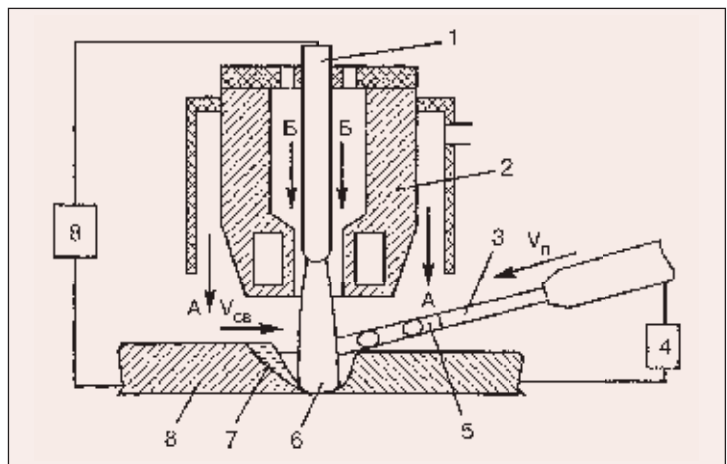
Схема плазменно-дуговой сварки с боковой подачей плавящегося электрода: 1 — электрод плазмотрона; 2 — сопло; 3 — плавящийся электрод; 4 — источник питания плазменной дуги; 5 — источник питания плавящегося электрода; 6 — плазменная дуга; 7 — дуга плавящегося электрода; 8 — изделие
